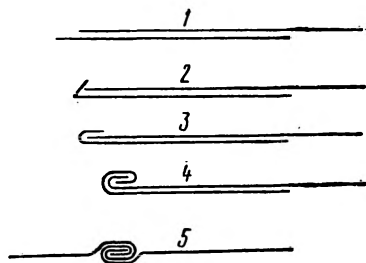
Заготовка двойного фальца по способу П. А. Лапшова
